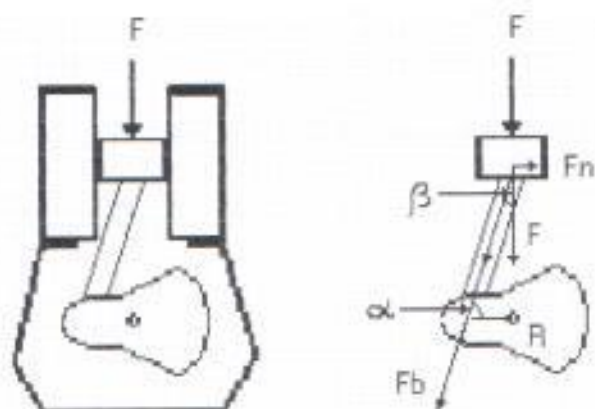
Descomposición de fuerzas en el sistema mecánico del motor
